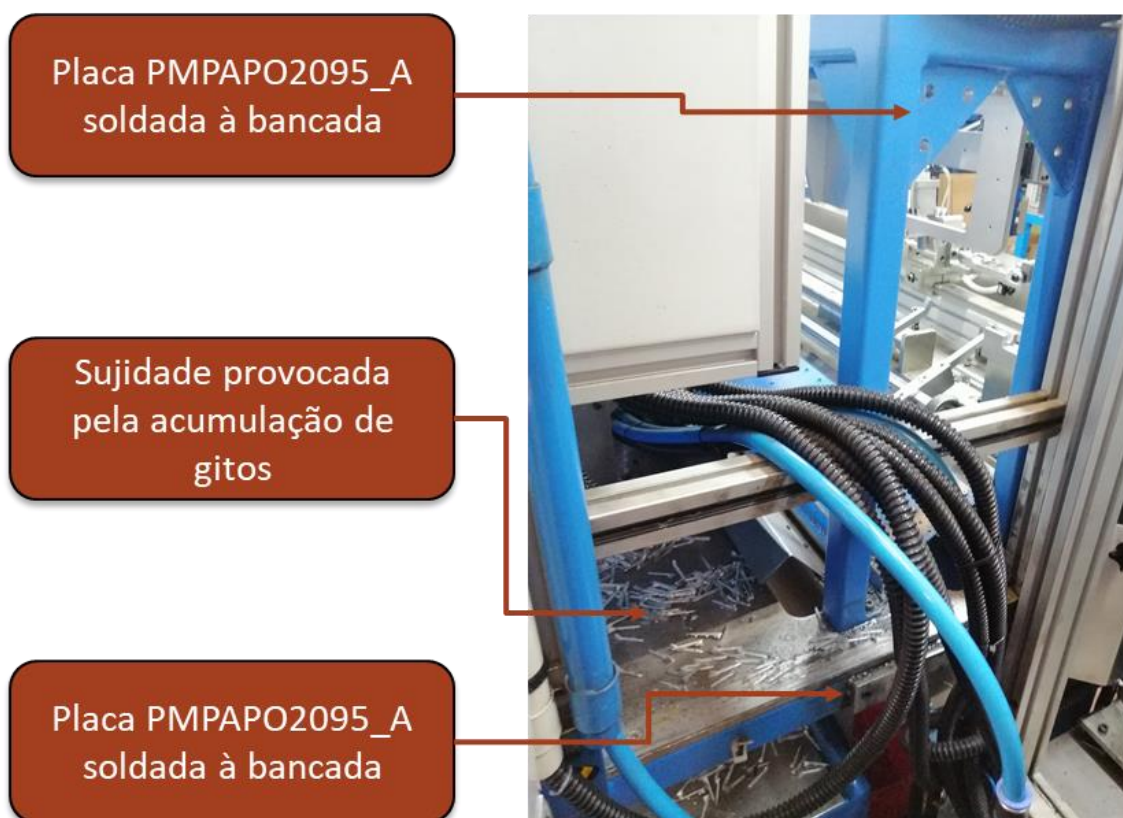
EMCC com furação concluída e placa PMPAPO2095_A soldada.
